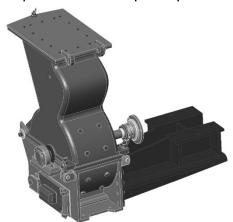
Общий вид разработанной конструкции молотковой дробилки
